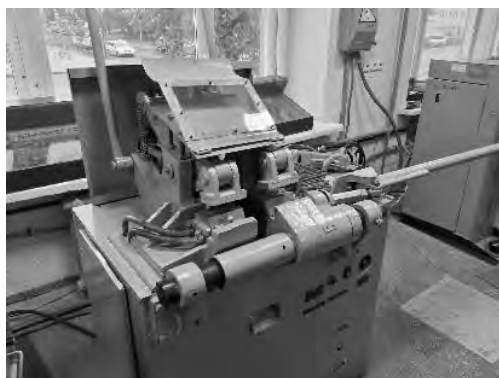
Машина для контактной стыковой сварки типа MS-1602У4
